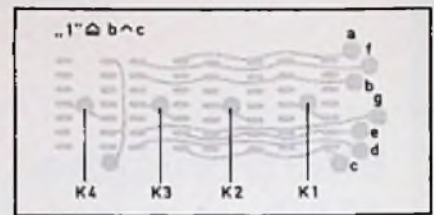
Bestückungszeichnung der Anzeigeplatine für DL 704
